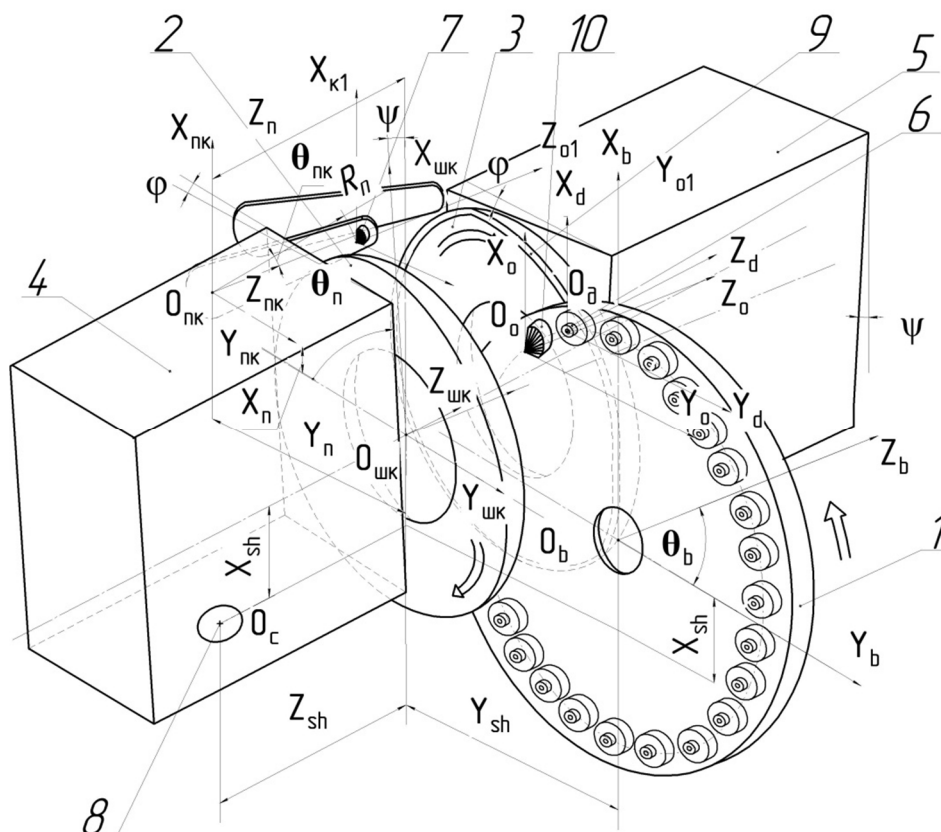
Розрахункова схема формоутворення торців хрестовин карданних валів
